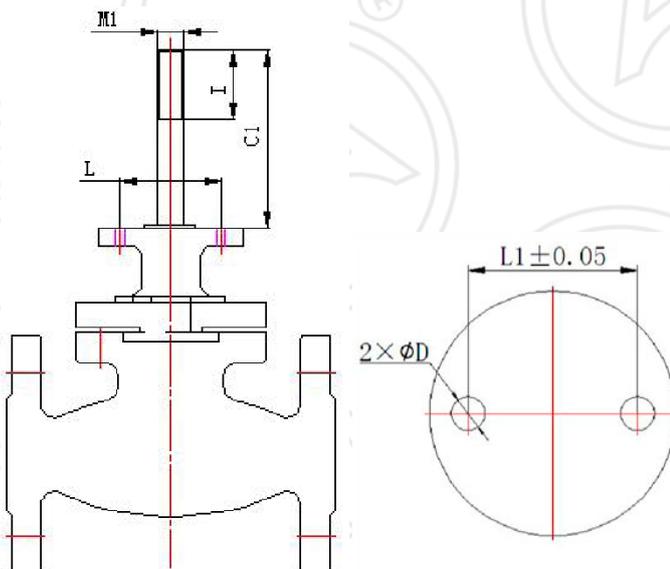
Присоединительные размеры привода ПЭП-СА3-1-(IN).
